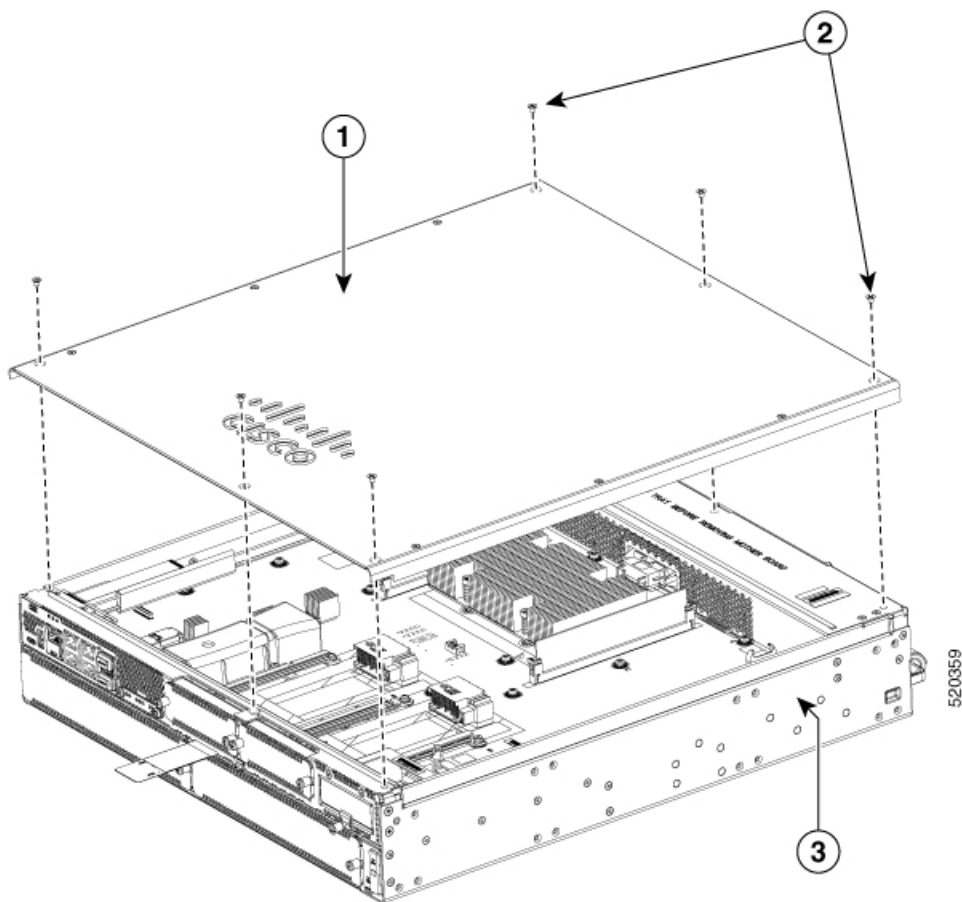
Instalación de la cubierta en de C8300-1N1S-4T2X|6T
